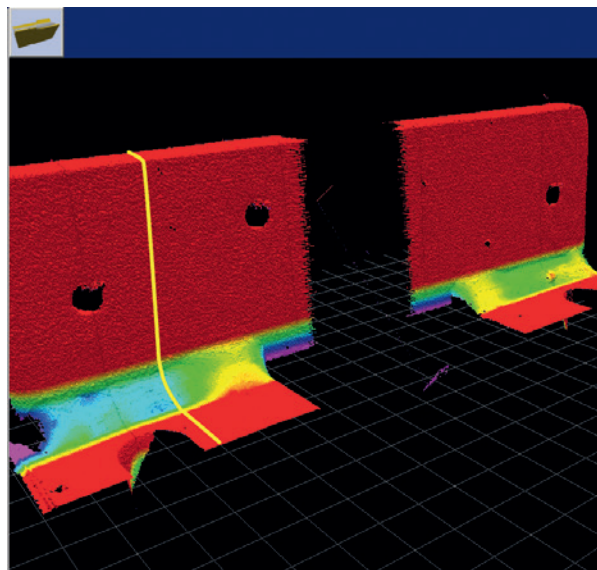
3D-Aufzeichnung der Schweißnaht durch Laserscanner (die rote Laserlinie ist gelb markiert), (mit freundlicher Genehmigung der MEL GmbH)
